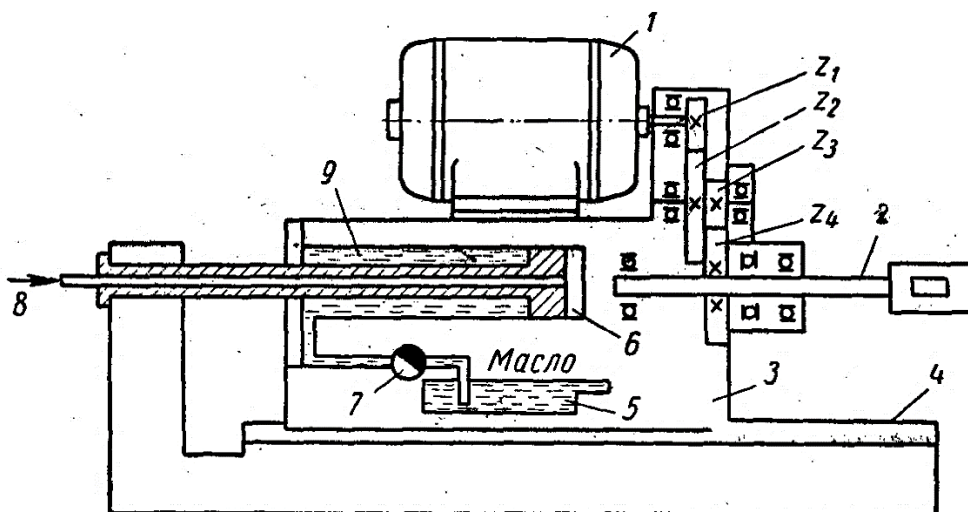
Схема силової головки з пневмогідравлічним приводом подачі
